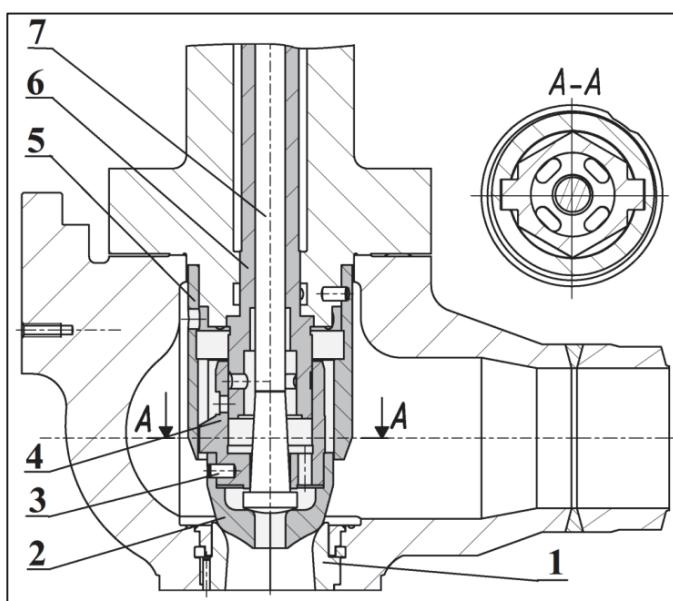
Регулирующий клапан №2 цилиндра высокого давления турбины К-200-130 новой конструкции
